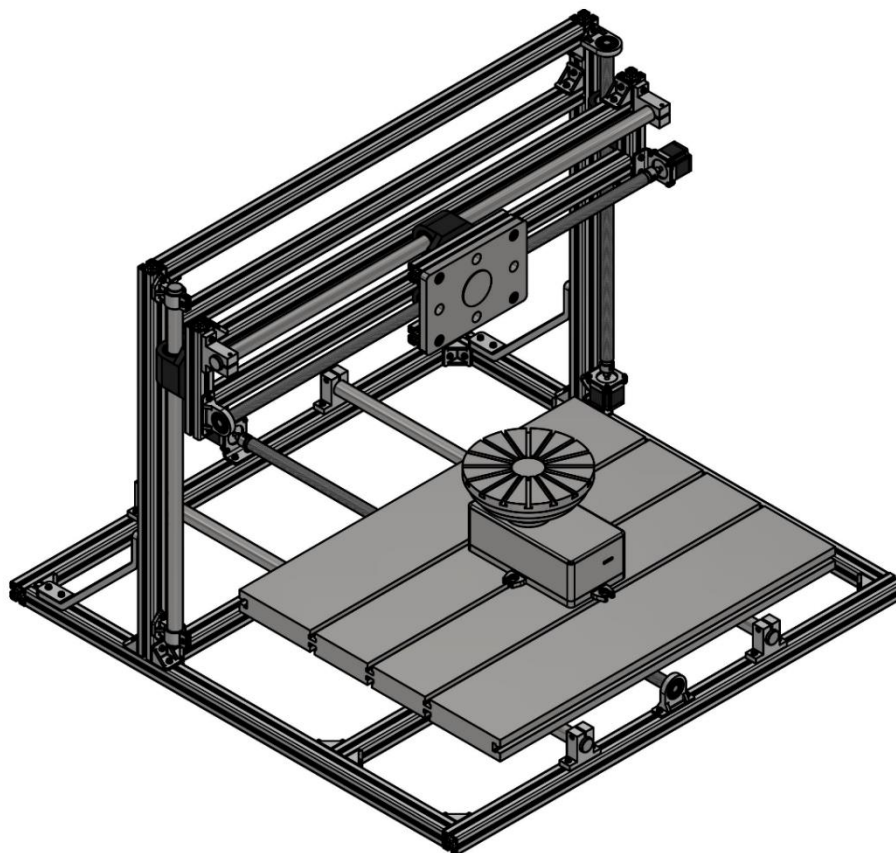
Загальний вигляд несучої системи гравіювального верстату з 4-ма керованими осями
